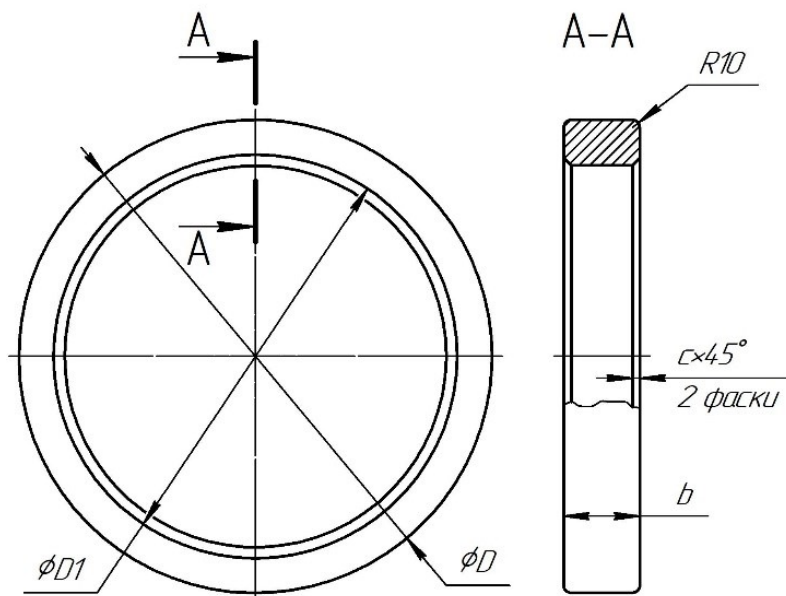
Типоразмера бандажей плавающего типа, исполнение – 1 по ОСТ 22-170-87
